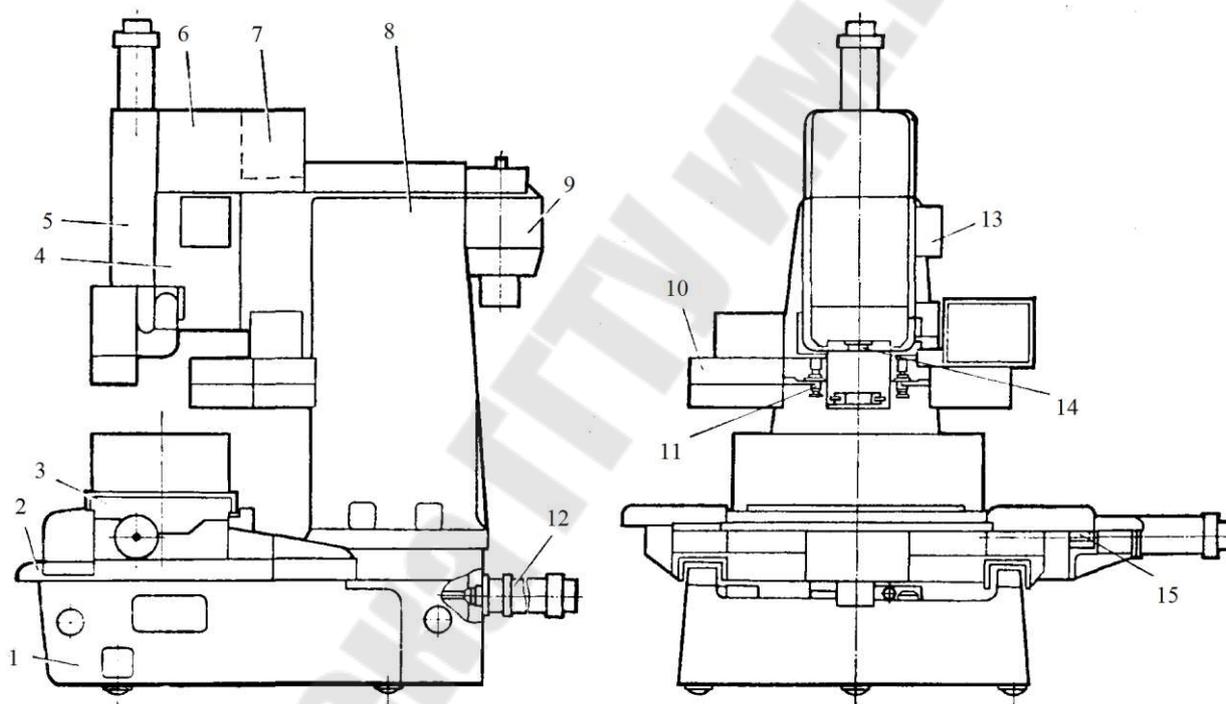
Общий вид координатно-расточного станка модели 2E450AФ1-1
